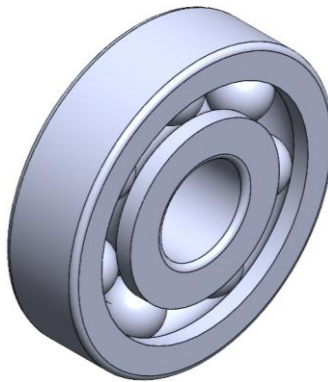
Modelo geométrico CAD 3D del rodamiento SKF 6405.
